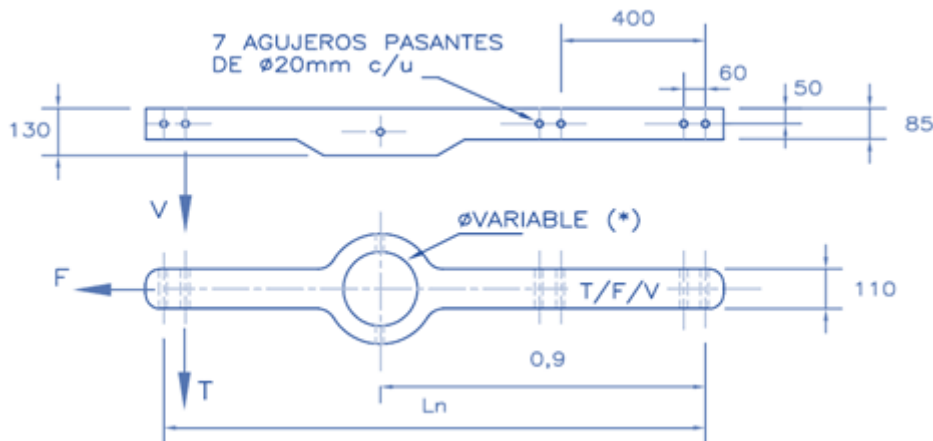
Geometría y dimensionamiento en mm de la cruceta asimétrica
